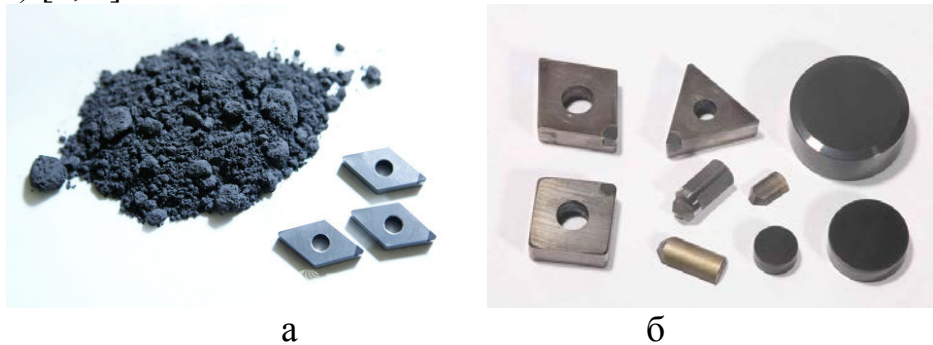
Кубический нитрид бора: а – внешний вид нанопорошка; б – внешний вид сменные многогранные пластины
